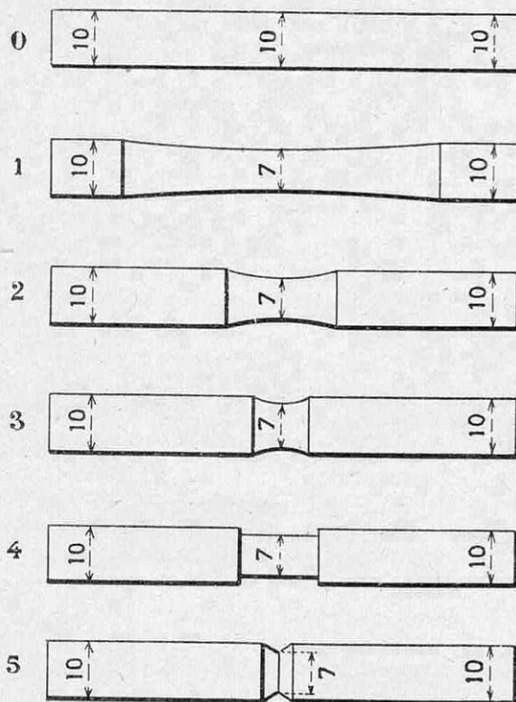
TYPES D'ÉPROUVETTES EMPLOYÉES PAR MOOR ET KOMMERS
